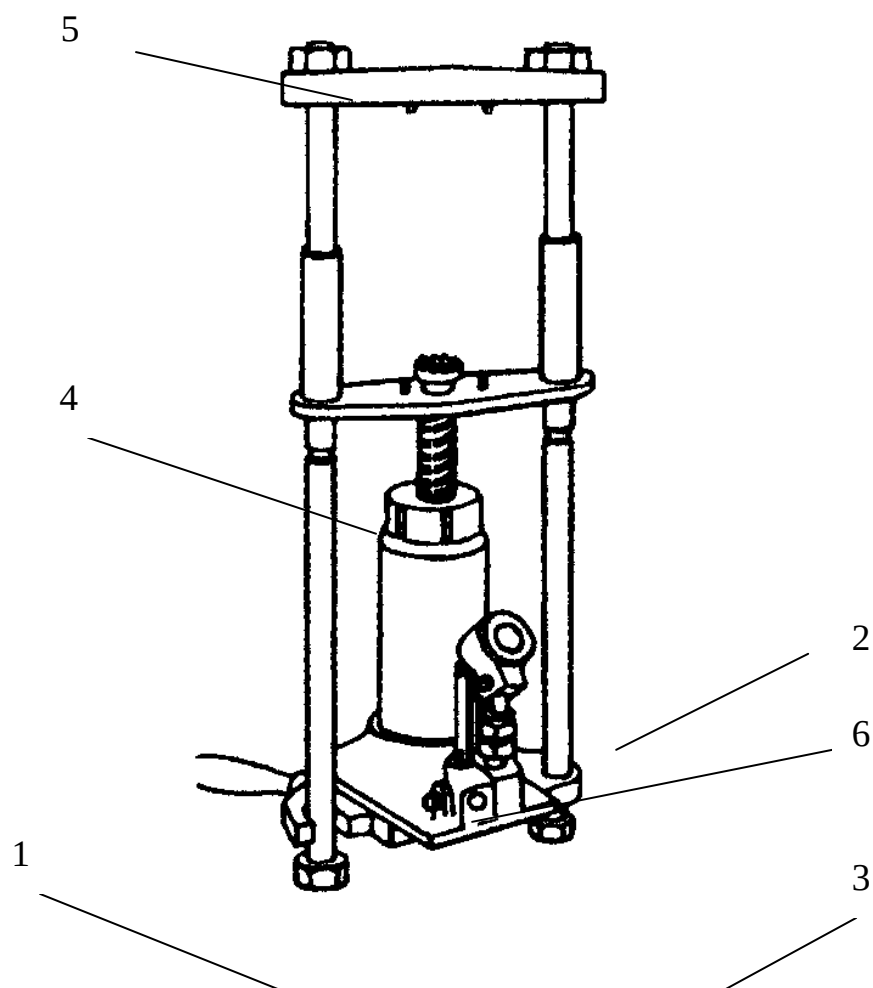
Съёмник для выпрессовки шкворня:
